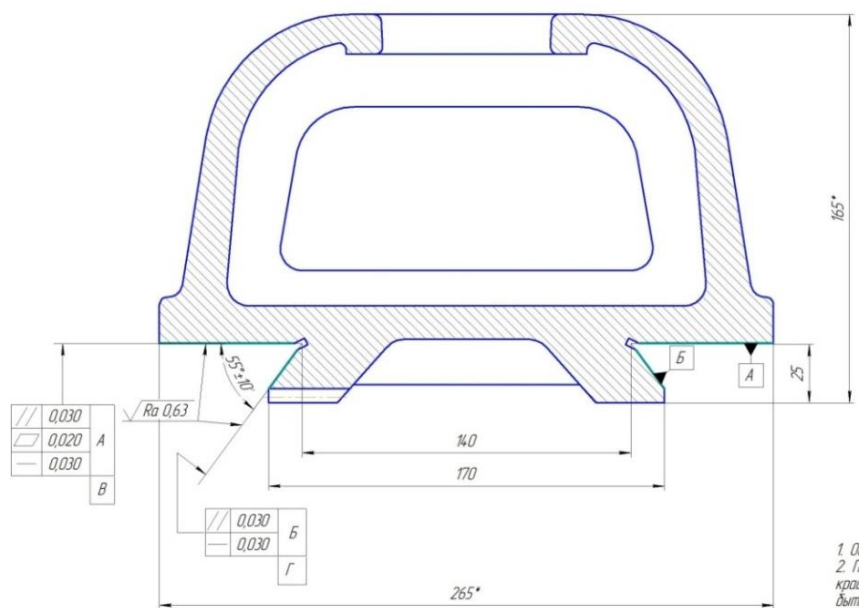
Рабочий чертеж хобота фрезерного станка
